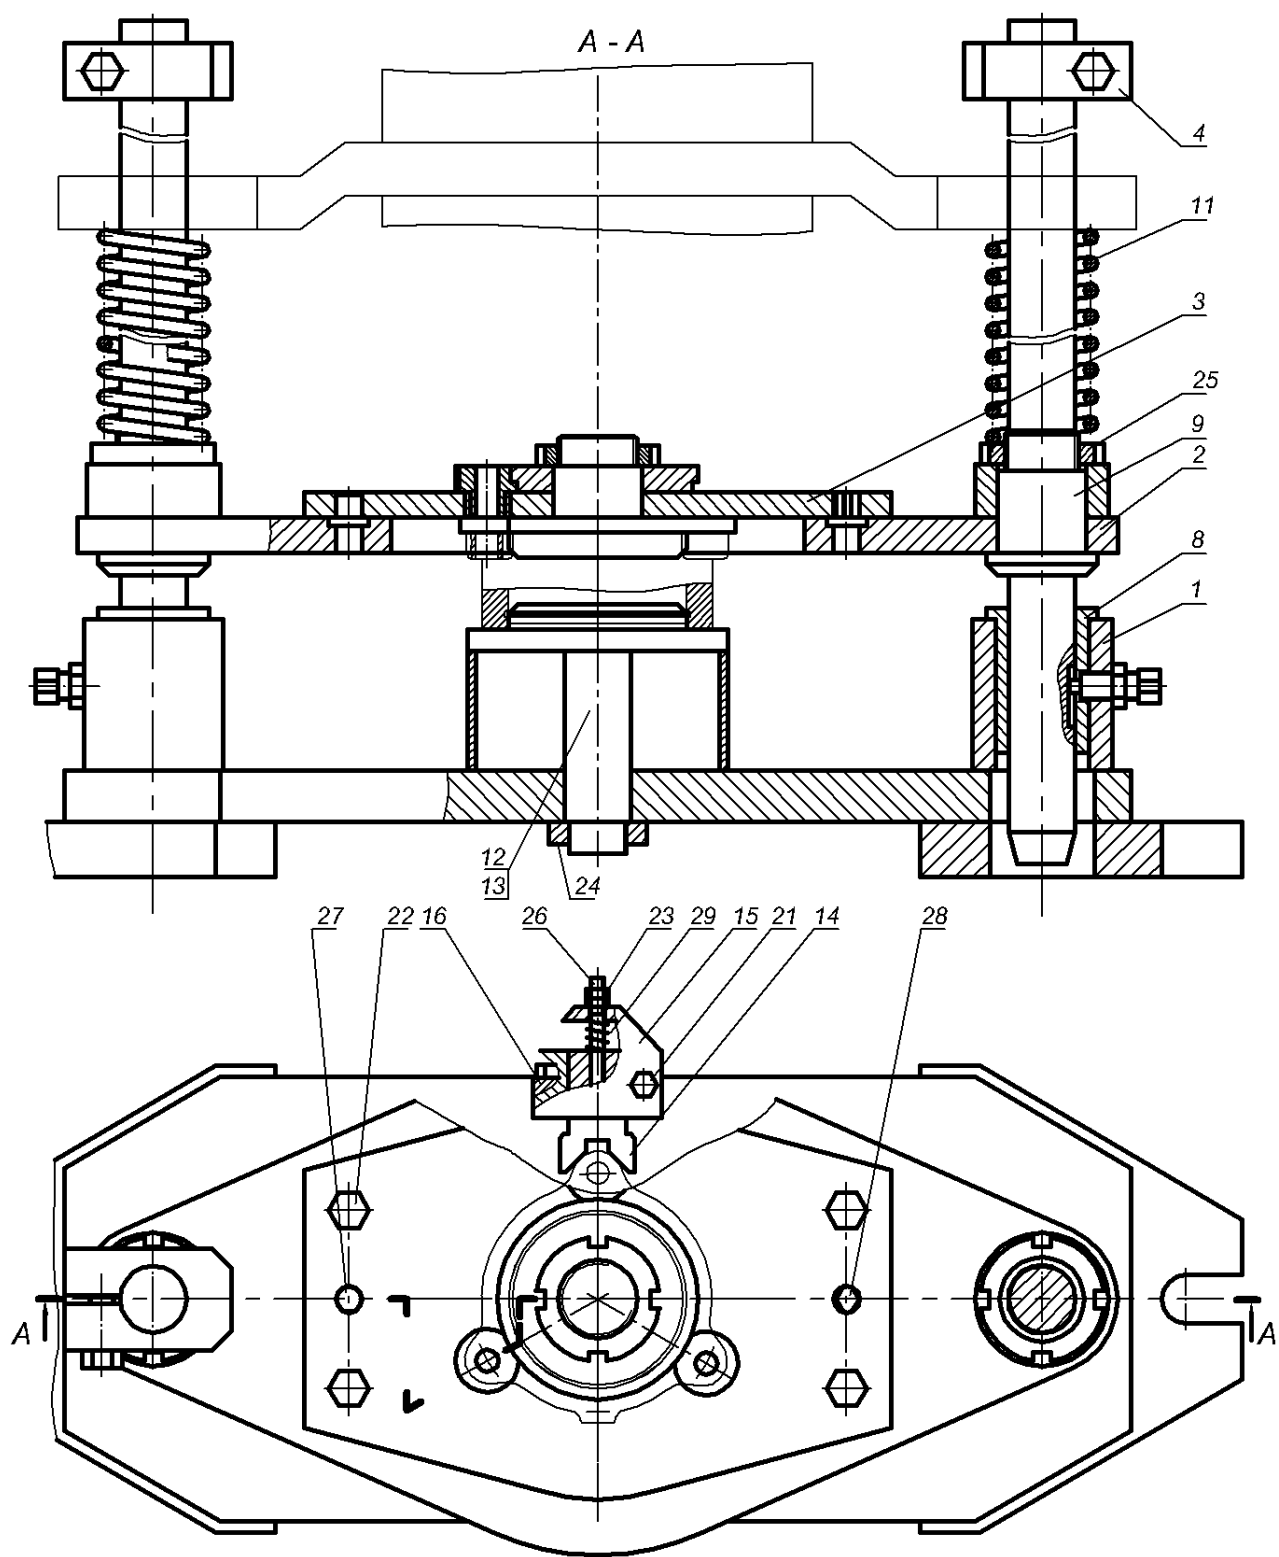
Кондуктор для одночасного свердління 3-х отворів Ø10 мм у деталі «Корпус підшипника 21-2501В»
